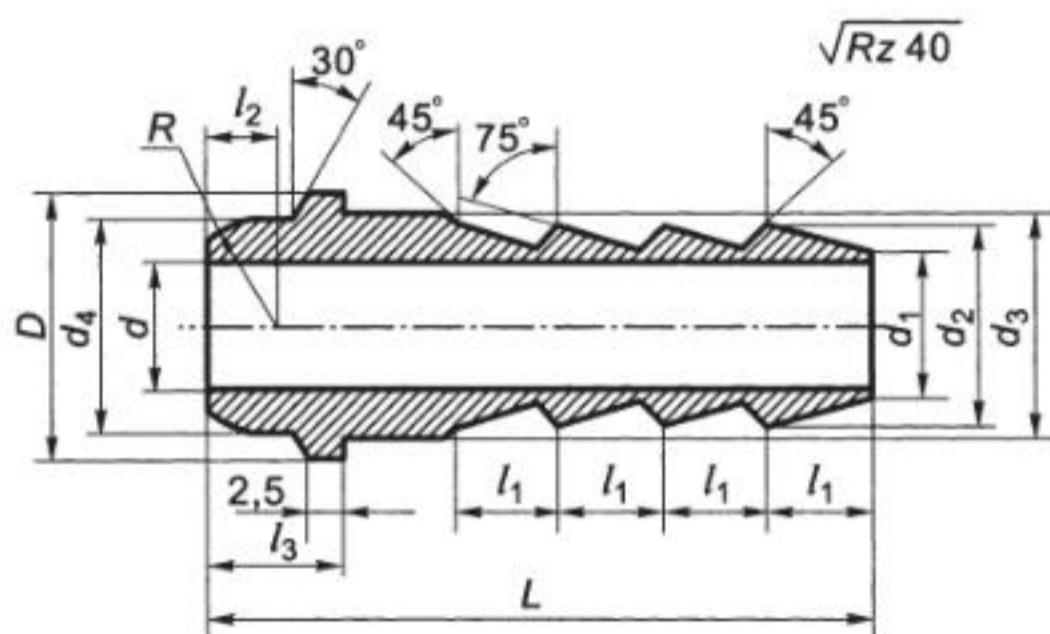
Ниппель для присоединения рукавов (шлангов)
